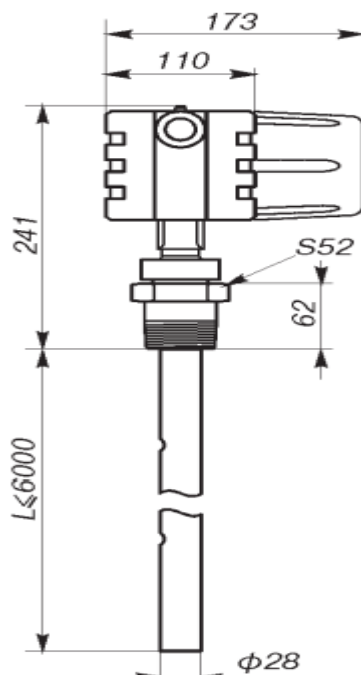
габаритные и установочные размеры Rosemount 3300
